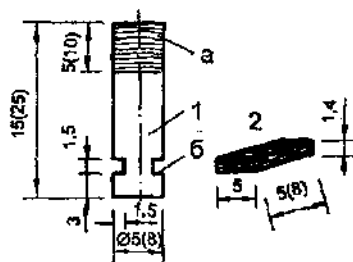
Шарнир для шкатулки: 1 — стержень; а — шероховатая (оцарапанная) часть, б — опоясывающая канавка, 2 — шпонка
